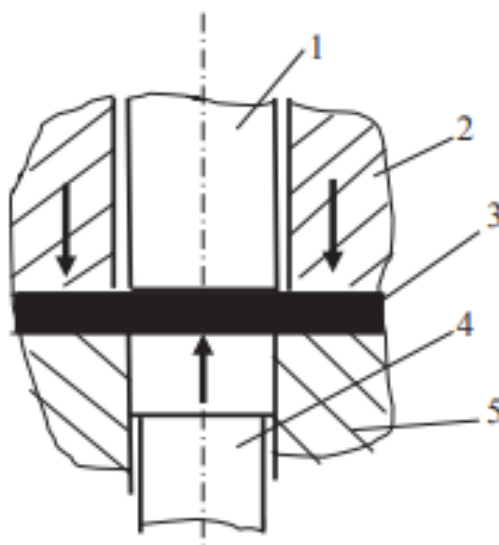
Схема чистовой вырубки (пробивки) с предварительным сжатием заготовки:
